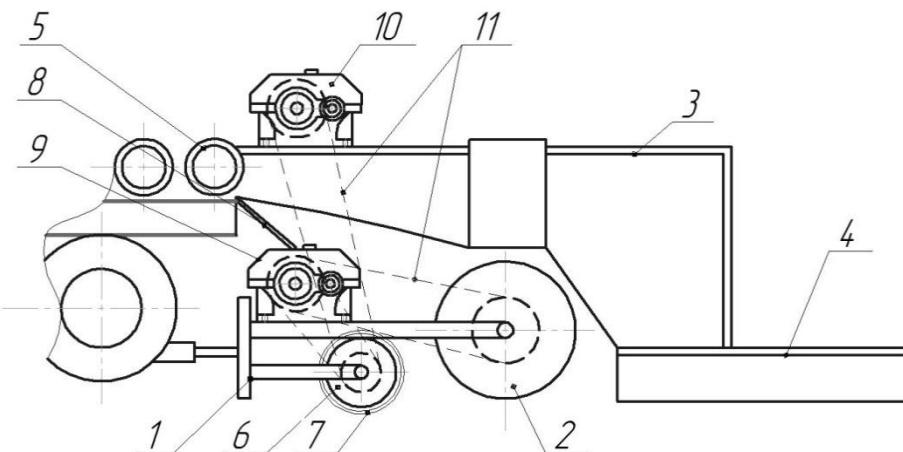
Схема катка-ложеобразователя лукоуборочной машины
